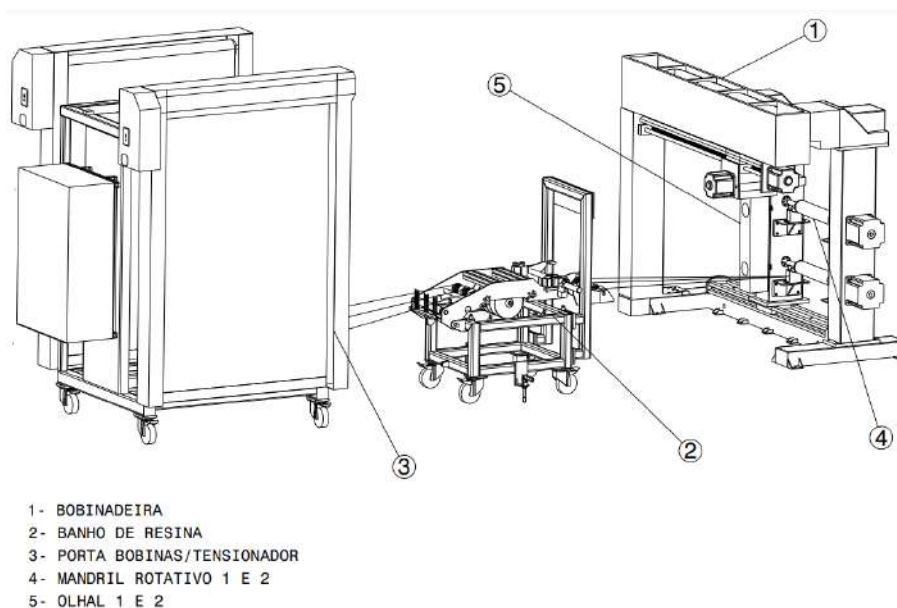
Máquina de bobinagem filamental, processo por banho de resina.
